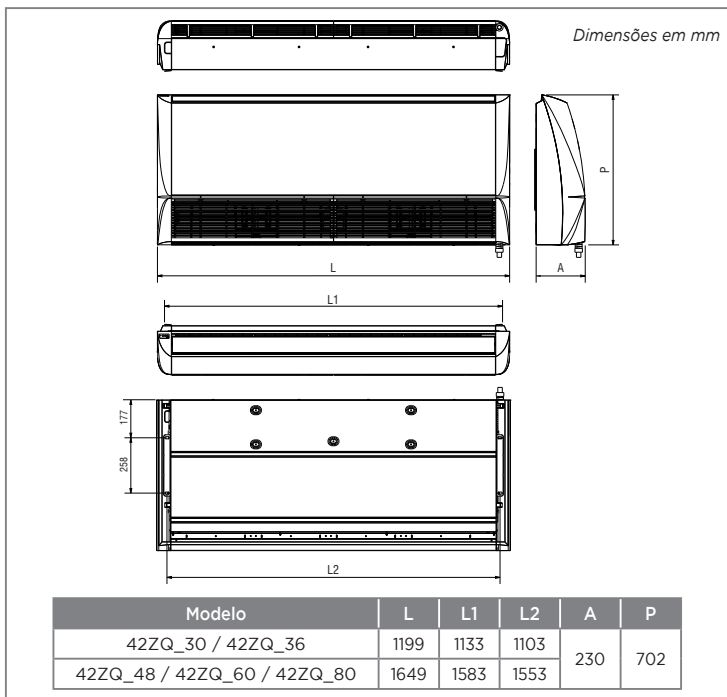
DIMENSIONAL UNIDADES EVAPORADORAS
